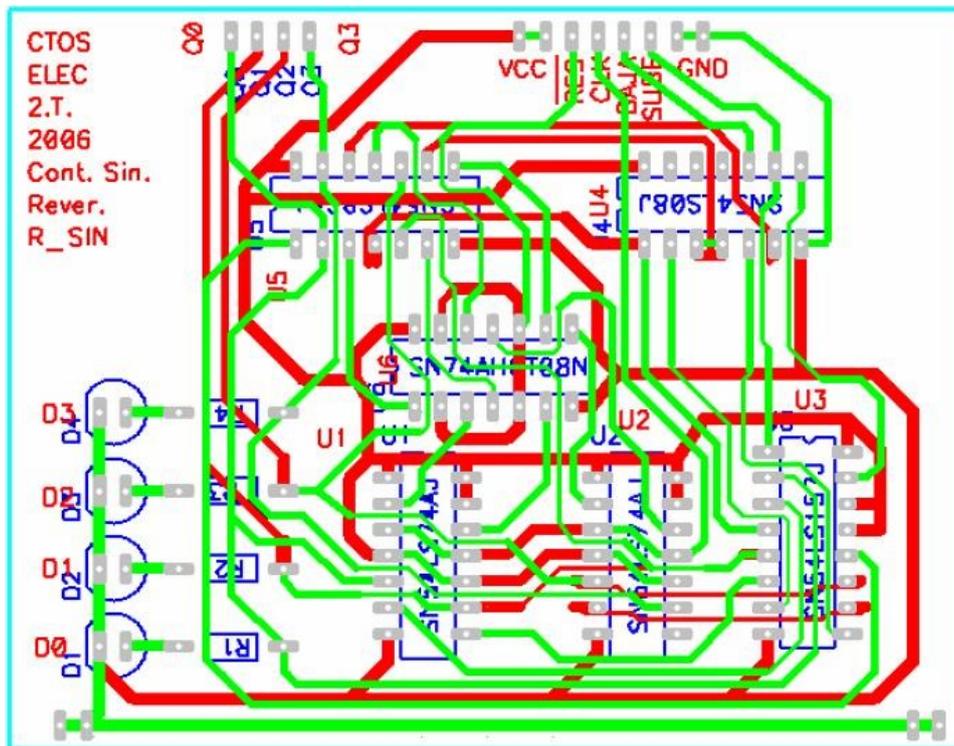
PCB de la placa que contiene un contador síncrono de 4 bits
